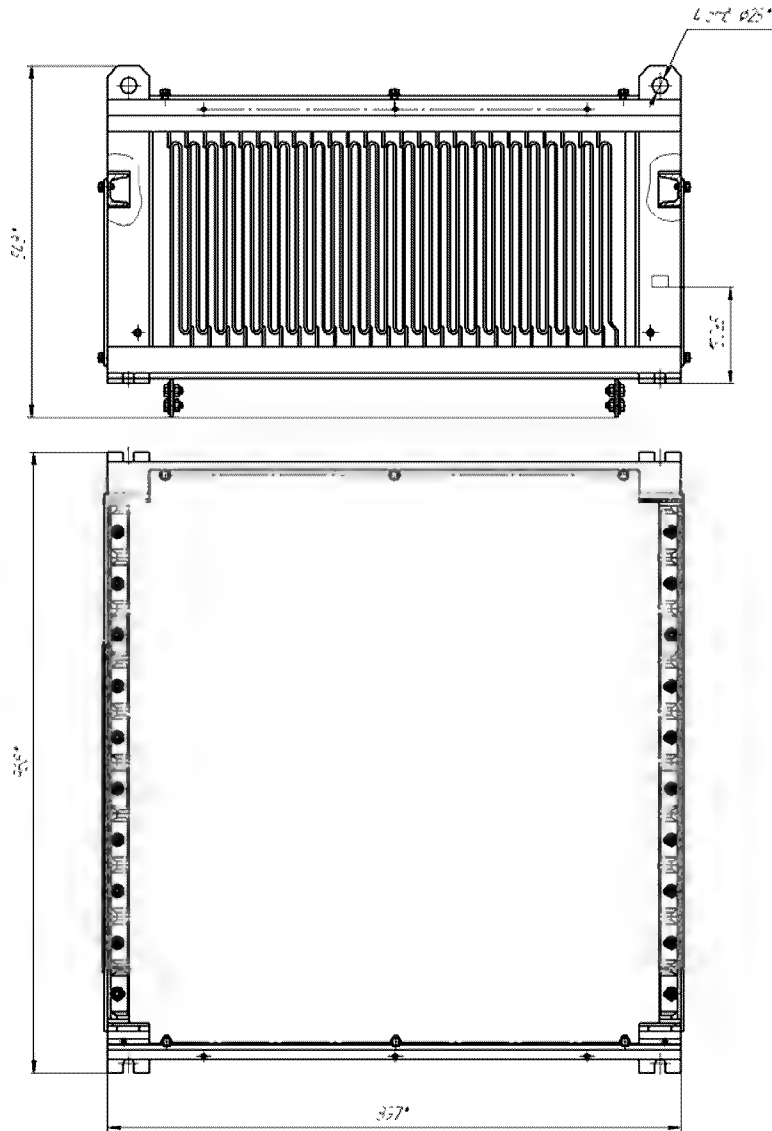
Габаритные размеры блока тормозных резисторов
